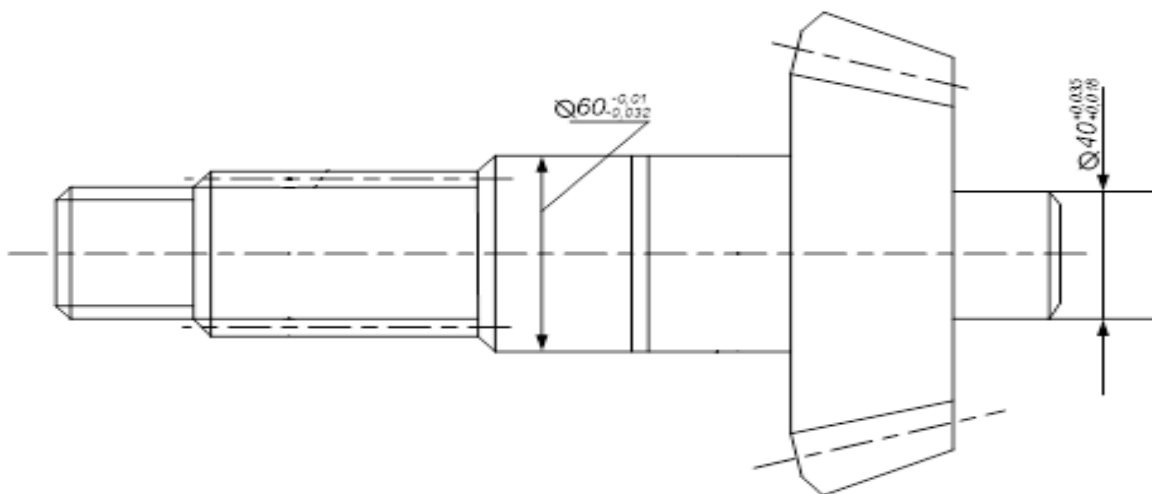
Ескіз ведучої шестерні редуктора заднього моста
